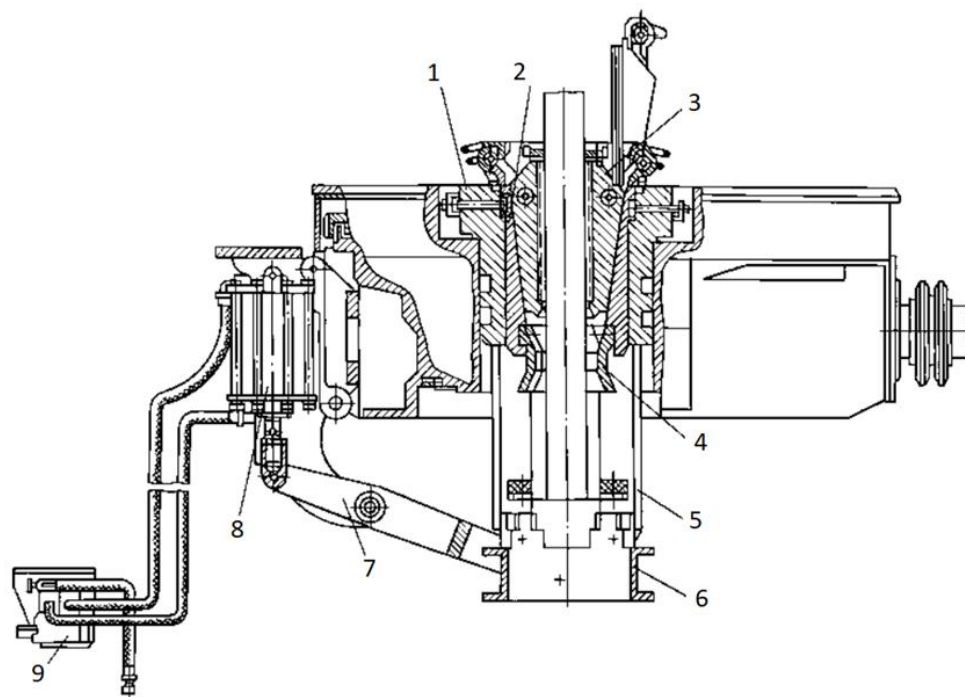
Клиновой пневматический захват ПКР560М: 1 - корпус; 2 - вкладыши; 3 - клинья; 4 - центратор; 5 - направляющие; 6 - кольцо; 7 - рычаг; 8 - пневмоцилиндр; 9 - педальный кран
